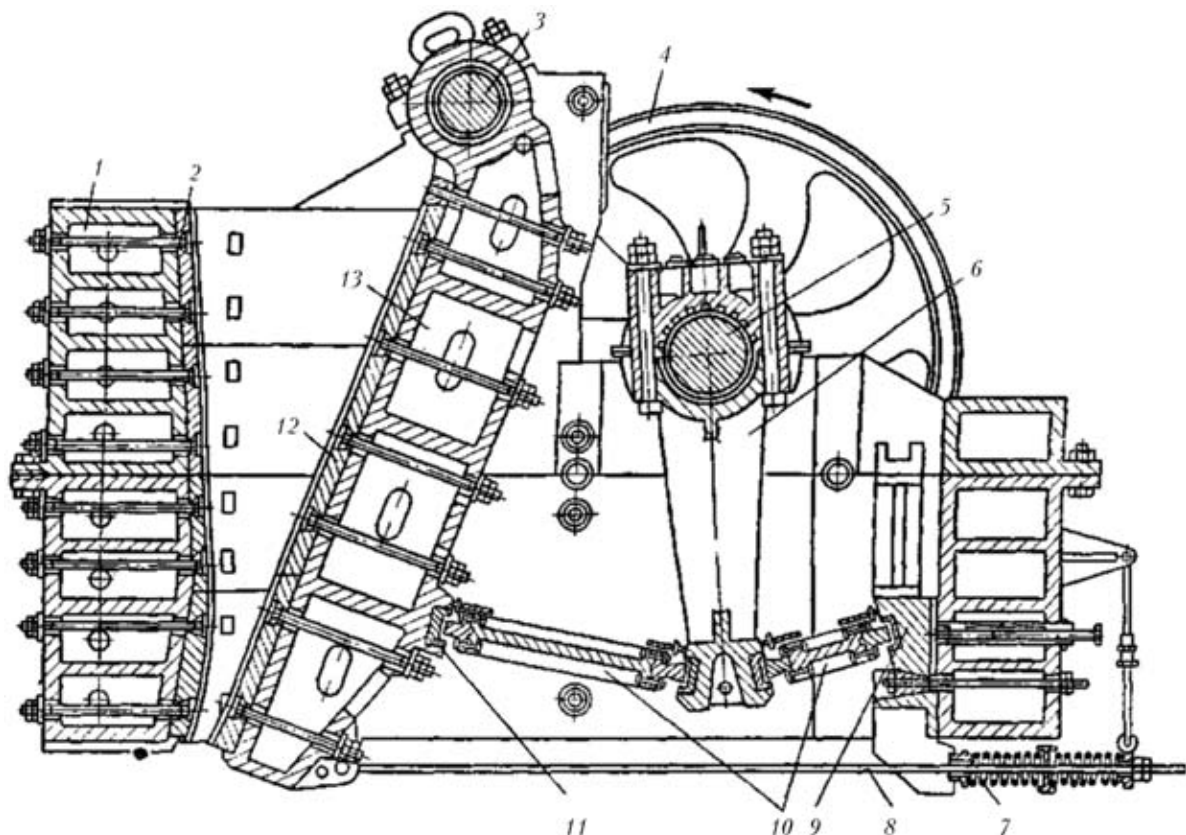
Схема щековой дробилки: 1 — станина; 2 — бронеплита на неподвижной щеке; 3 — ось; 4 — маховик; 5 — эксцентриковый вал; 6 — шатун; 7 — пружина; 8 — тяга; 9 — регулировочное устройство; 10 — распорные плиты; 11 — вкладыши; 12 — бронеплиты; 13 — подвижная щека
